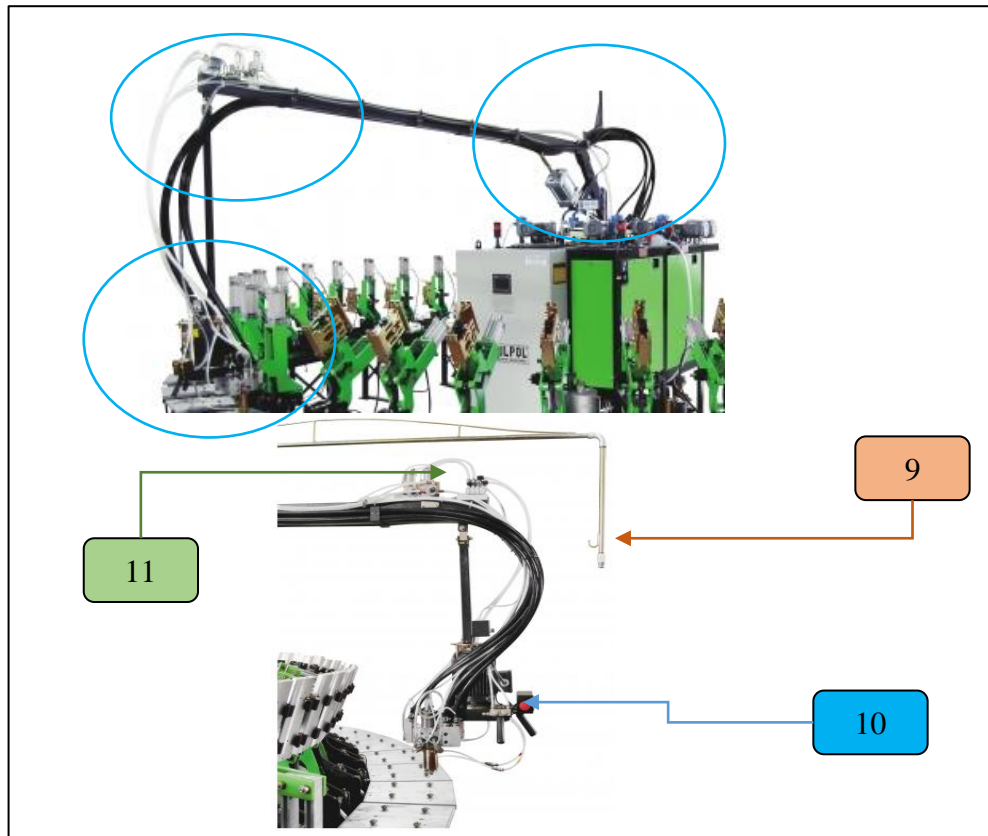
Conjunto de sistemas de la máquina inyectora [30].
